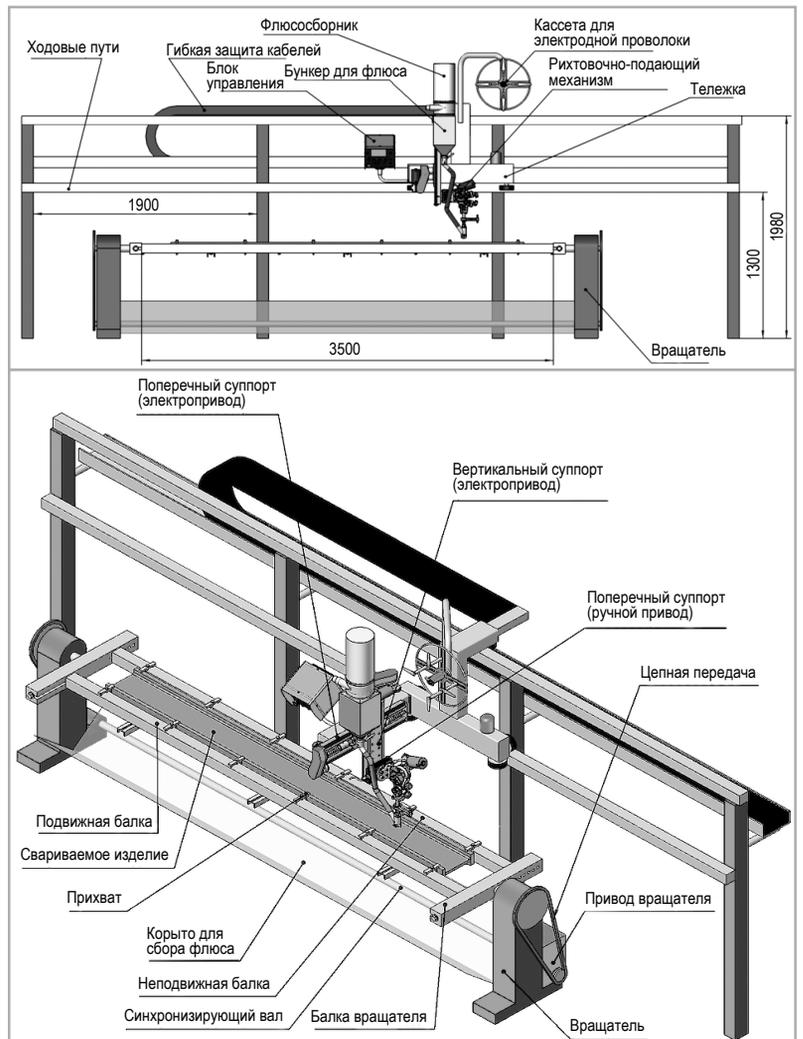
Установка для сварки двутавровых балок спекательных тележек – общий вид и комплектация
